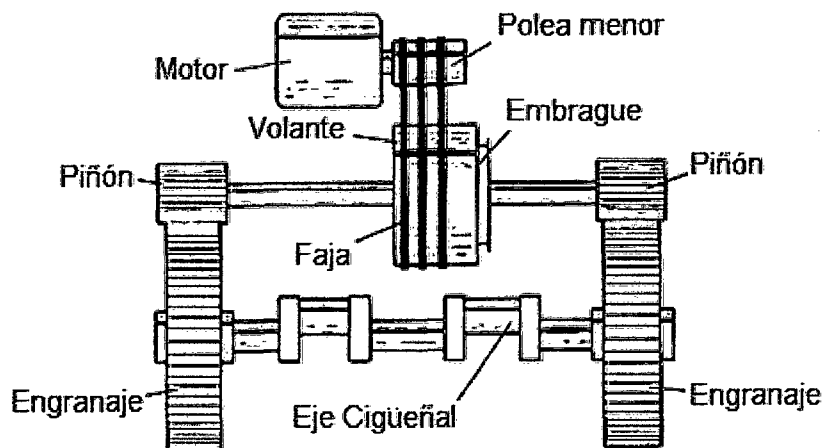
Sistema de trasmisión engranado en ambos extremos del eje cigüeñal.
